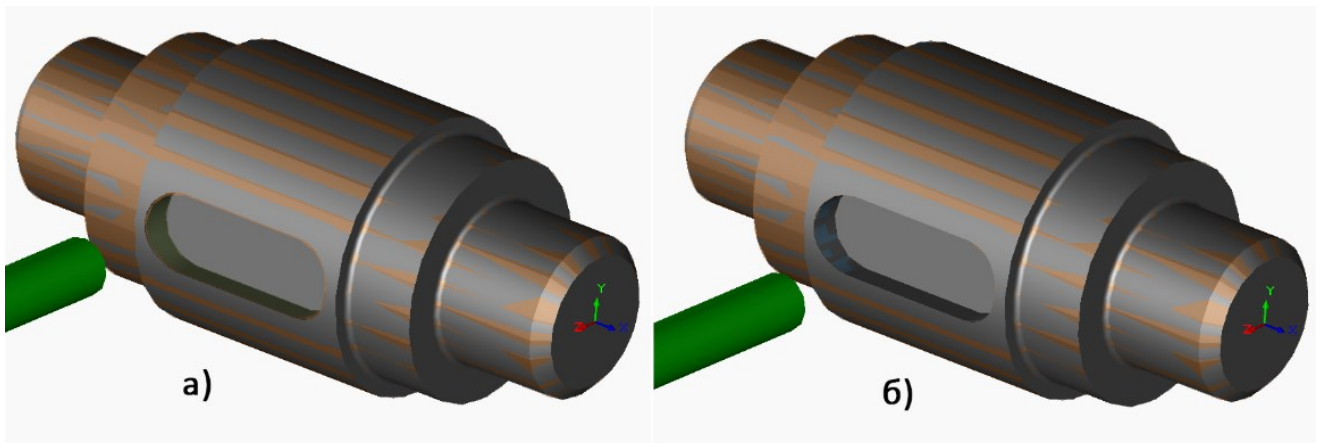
Фрагменти імітації процесу обробки: а) свердління, б) контурне фрезерування, Фрезерний установ.
